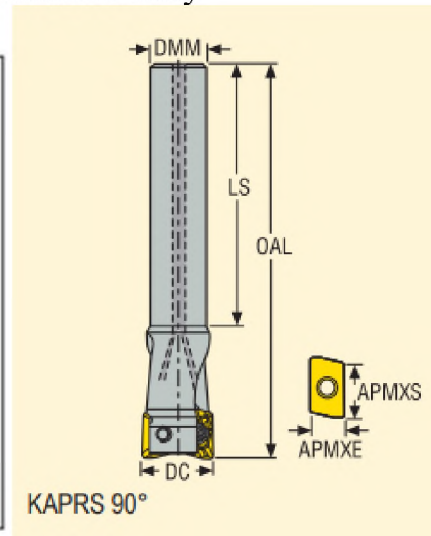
Фреза R217.69-1012.0-06-2N [7 с.23]
